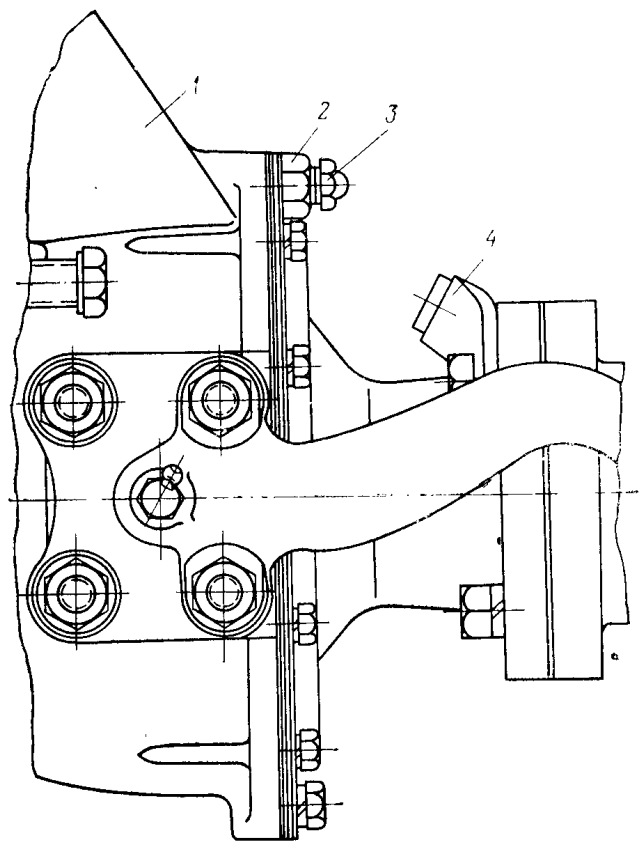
Установка упора-ограничителя поворота колес автомобиля УАЗ-452:
